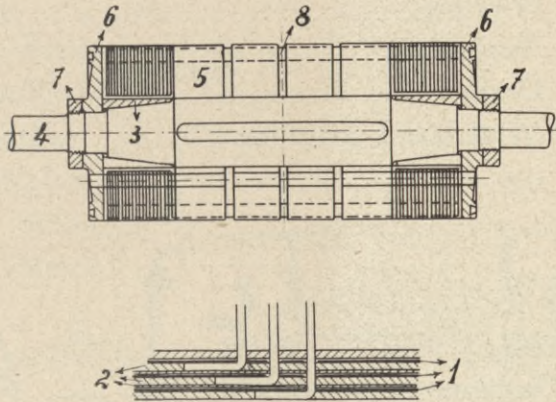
Siehe auch E. P. 13051 (Jahr 1904).
